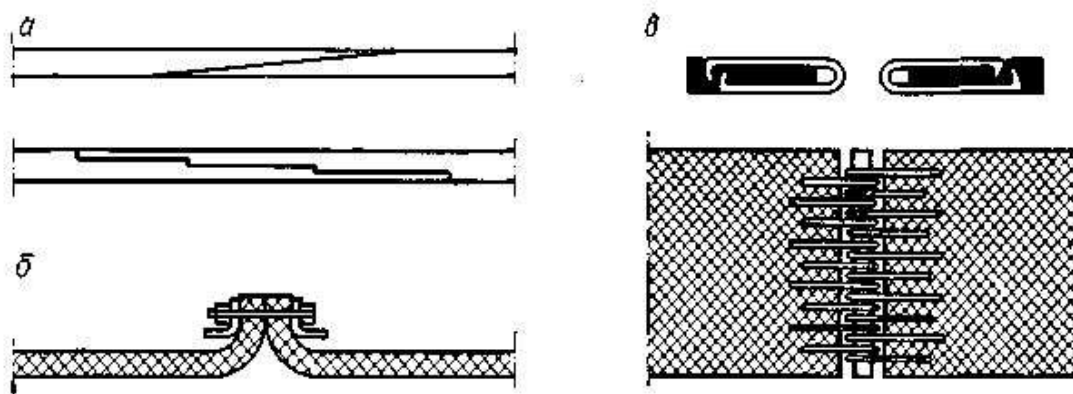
21 – Соединение концов ремня: а – склеивание с косым и ступенчатым срезом; б – жесткое металлическое соединение; в – шарнирное металлическое соединение
